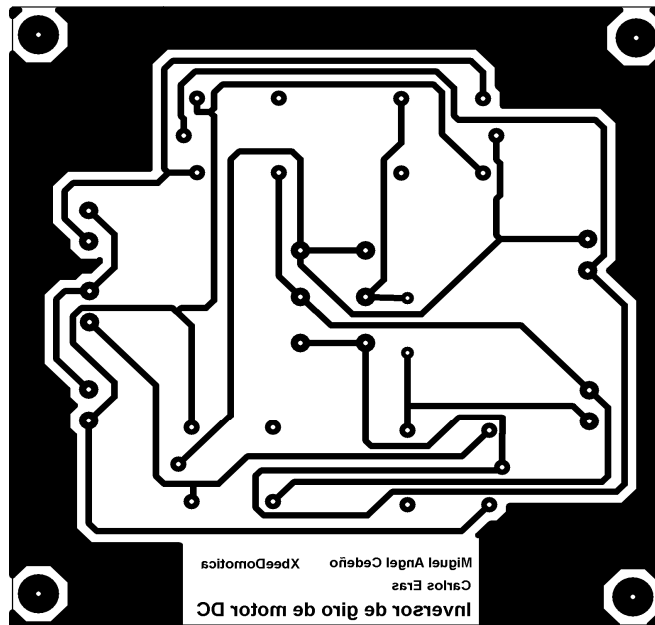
Bottom copper (Cobre inferior) Circuito inversor de giro de motor DC
